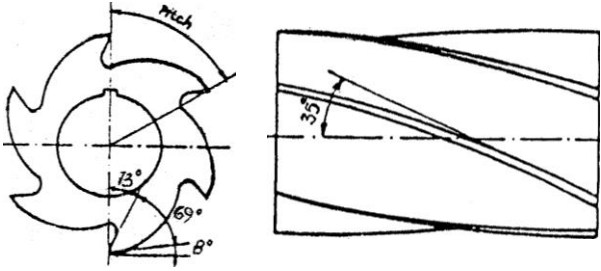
Pisau Frais Mantel (*Plane Milling Cutter*)
